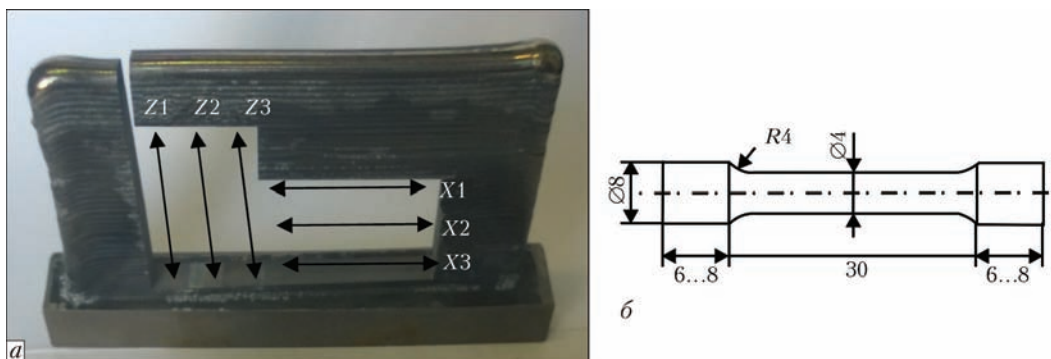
Схема вырезки образцов для механических испытаний (*a*), чертеж образца (*б*)
